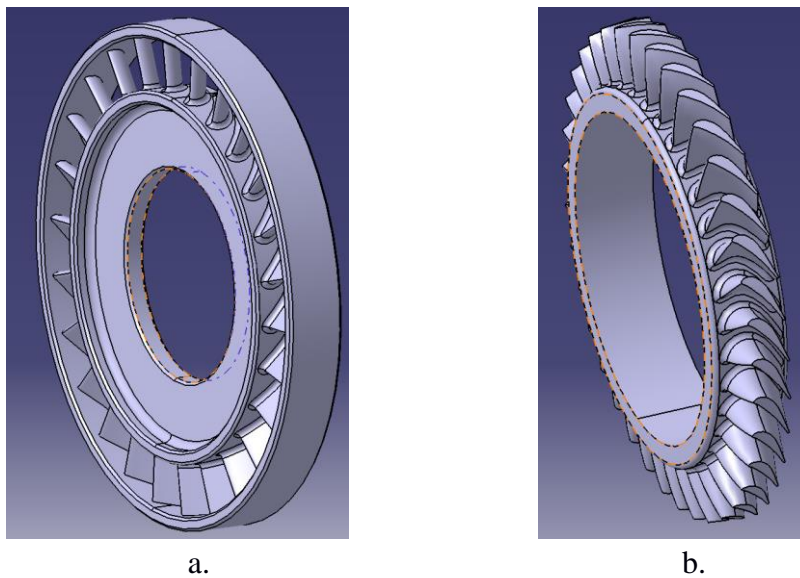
Rețele turbină de mici dimensiuni: a. statorul, b. rotorul
